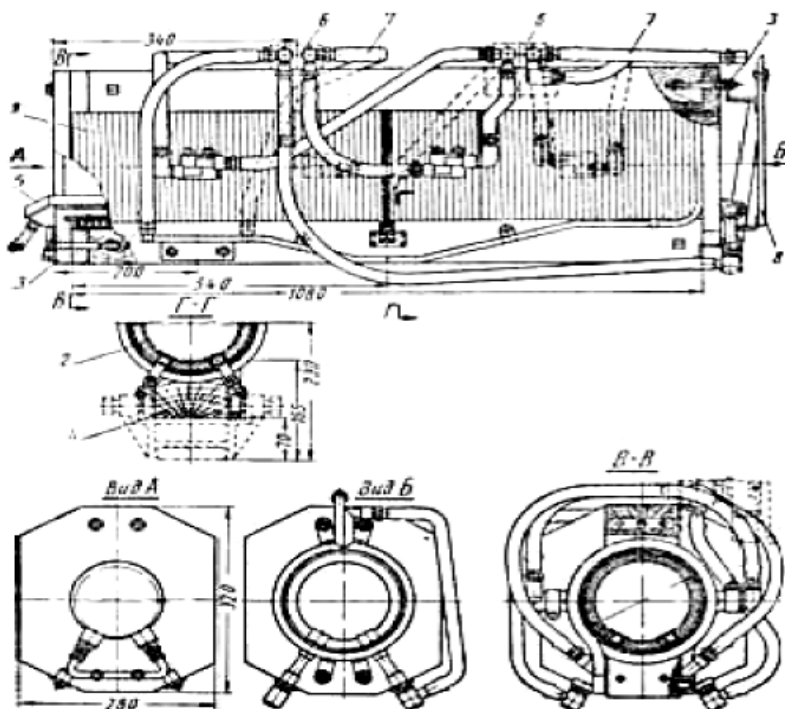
Многовитковый цилиндрический индуктор с несущими брусками:
